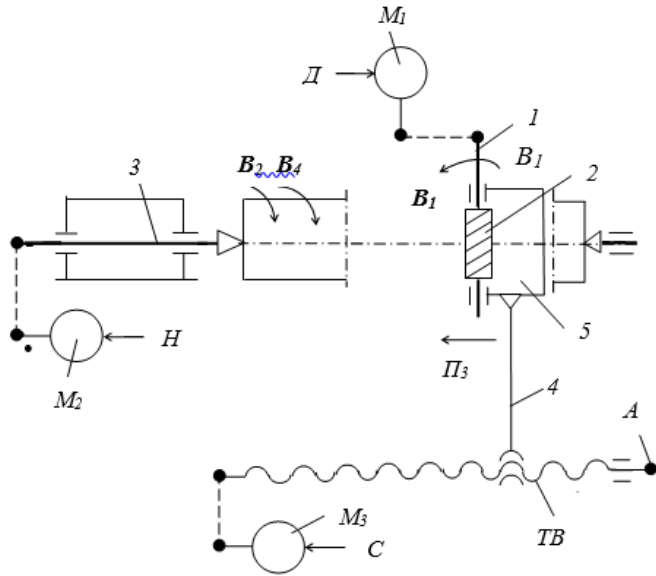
Исполнительные органы гибридной структурной схемы шлицефрезерного станка
